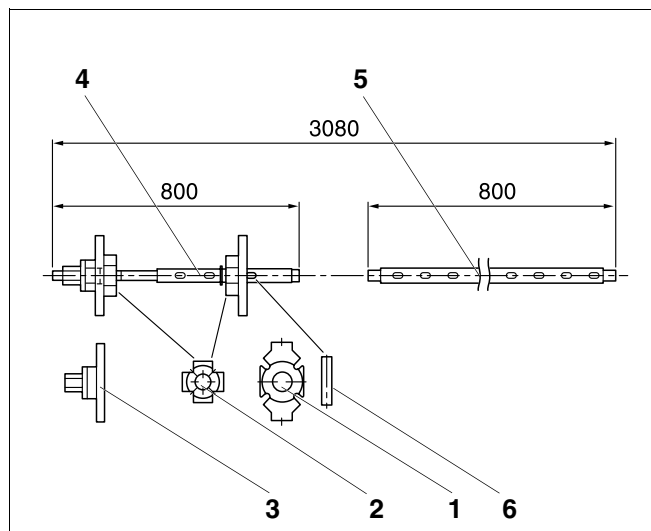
Outillage de serrage pour chaudière, taille 2.3
